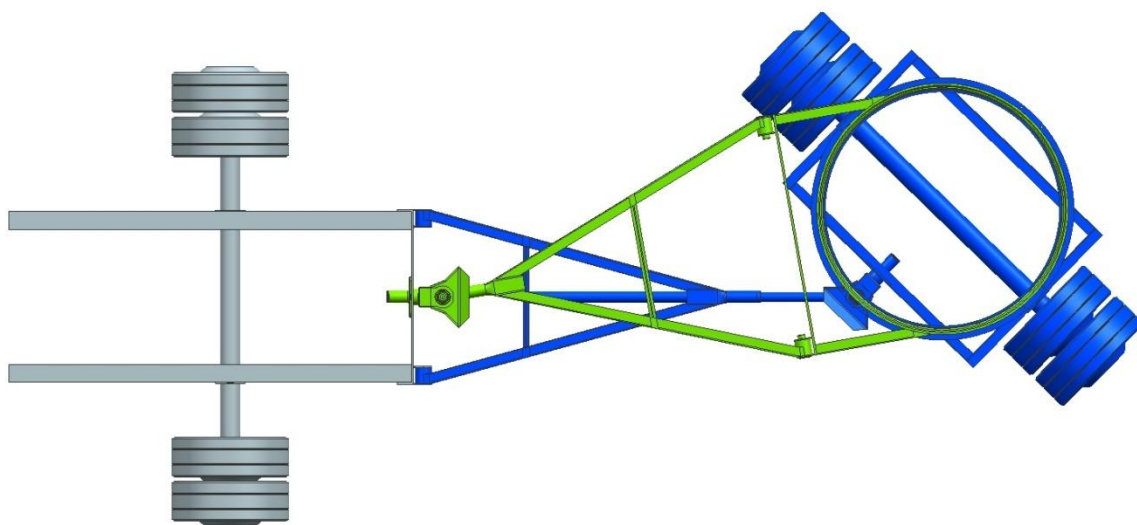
vzájemný pohyb soustavy spojení
